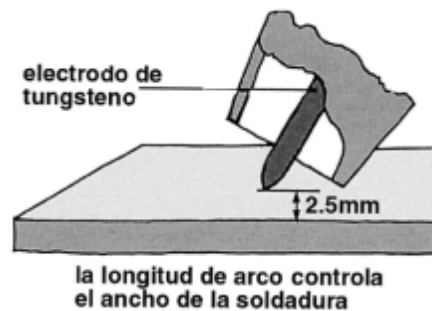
Longitud del arco soldadura TIG.
